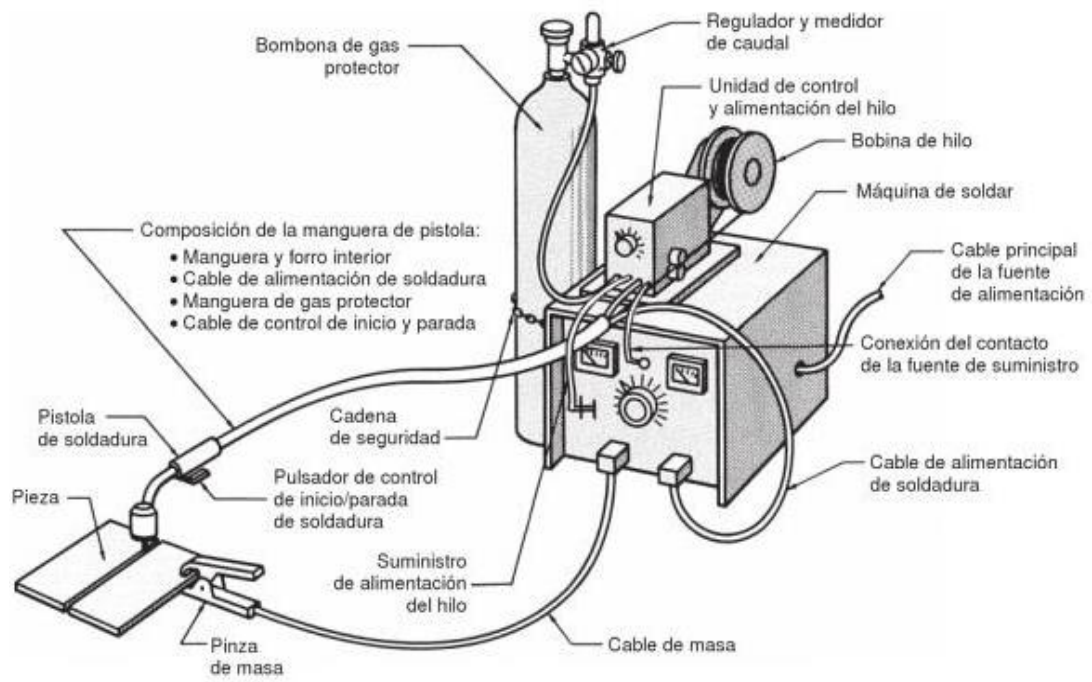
Esquema básico de un equipo para soldadura MIG
